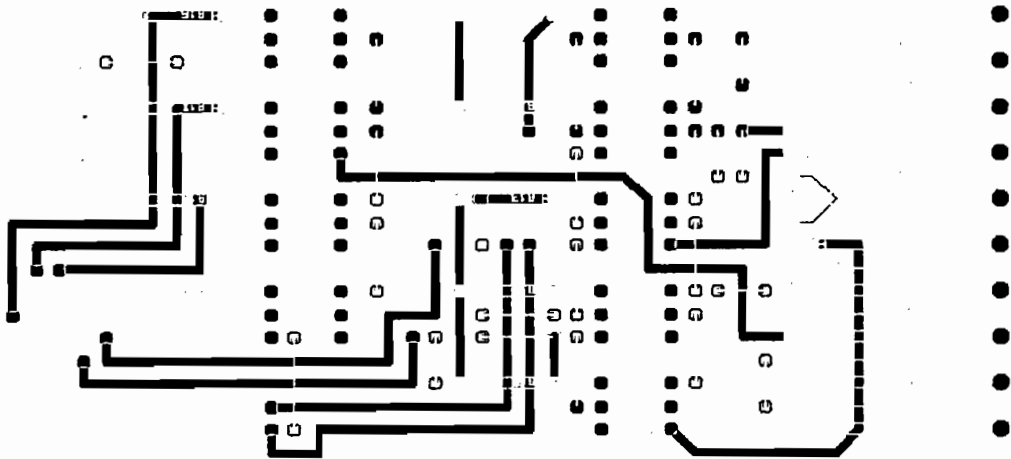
Tarjeta de entradas digitales, lado de soldadura
